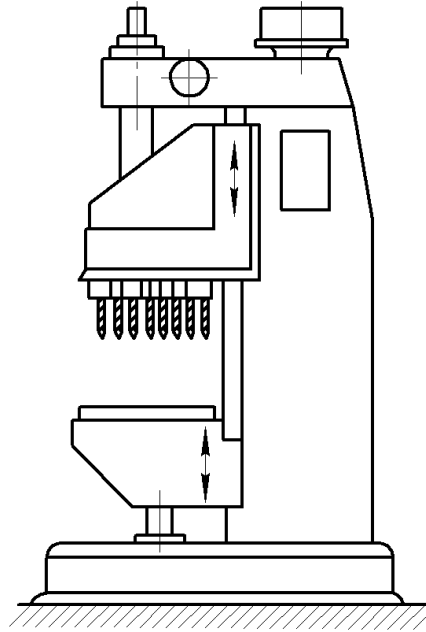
Вертикально-свердлильний багатошпindelний верстат
